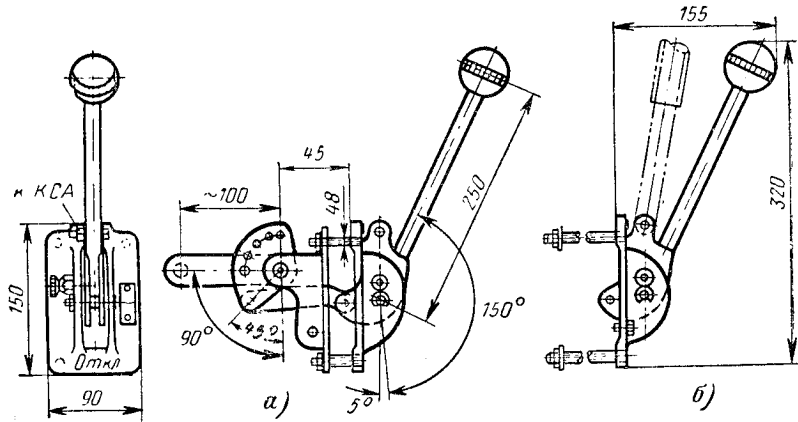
Привод ручной рычажный типа ПР-2.
